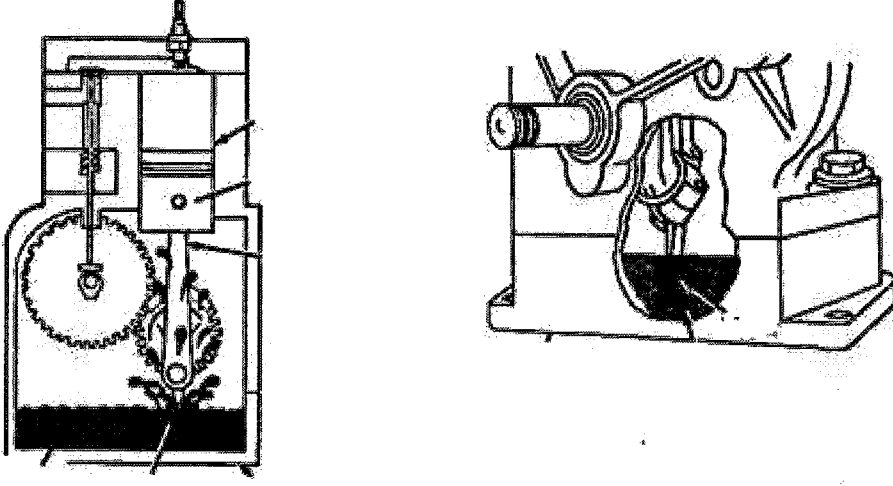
Pistonlu yağ pompası (Miller & Miller, 1993)
